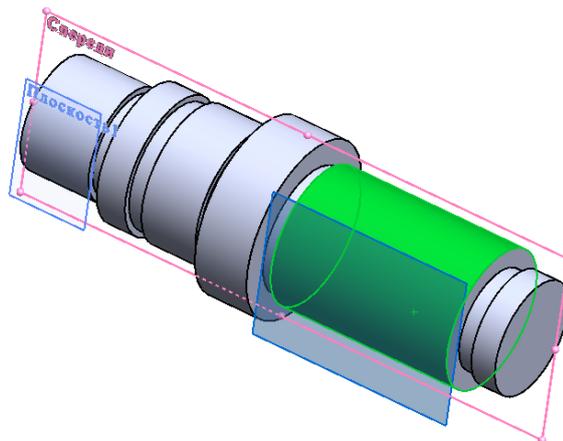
Створення допоміжної площини для побудови шпоночного пазу на поверхні деталі обертання
